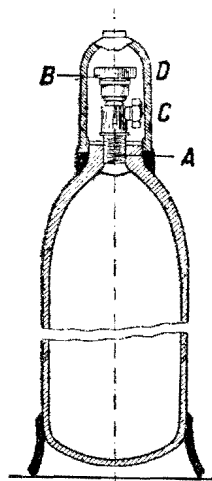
Баллон для хранения сжатого газа: *A* — винтовая нарезка; *B* — запорный вентиль; *C* — штуцер для привинчивания манодетандера или трубки для присоединения резиновой кишки; *D* — колпак.
